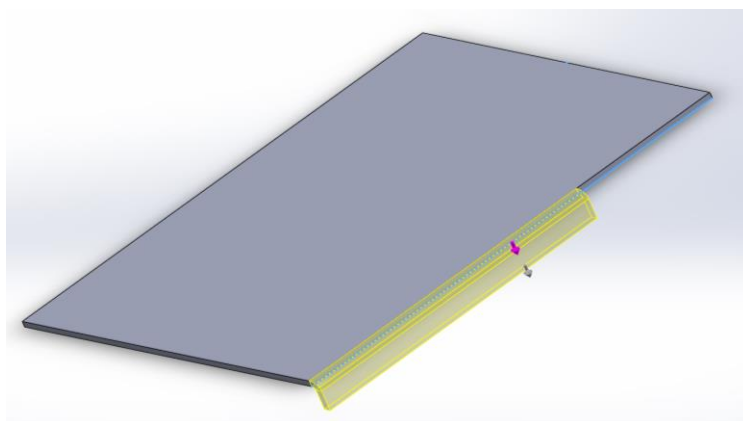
Rezultatul obținut în urma utilizării comenzii *Edge Flange
